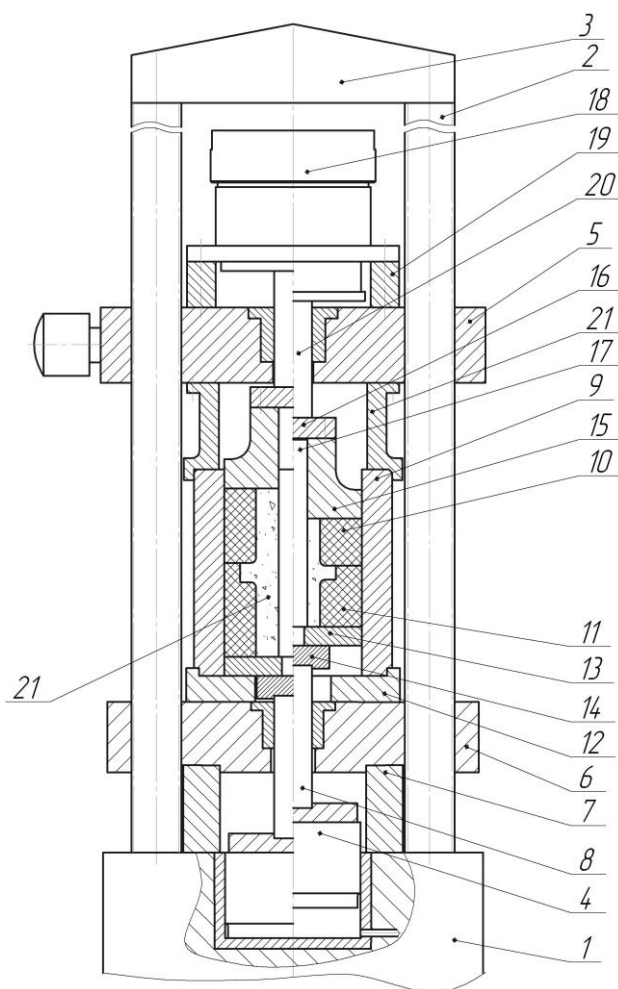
Принципиальная схема установки для эластостатического прессования двустороннего действия: 1 — станина установки; 2 – направляющие колонны; 3 – верхняя неподвижная плита; 4 – плунжер гидроцилиндра; 5 – подвижная траверса; 6 – нижняя неподвижная плита; 7 – промежуточная опора; 8 – шток; 9 – контейнер; 10 – эластичный элемент верхний; 11 – эластичный элемент нижний; 12 – опорная подвижная плита; 13 – пуансон нижний; 14 – пуансонодержатель нижний; 15 – пуансон верхний; 16 – пуансонодержатель верхний; 17 – оправка; 18 – дополнительный силовой гидроцилиндр; 19 – промежуточная опора; 20 – плунжер гидроцилиндра; 21 – порошковый материал
